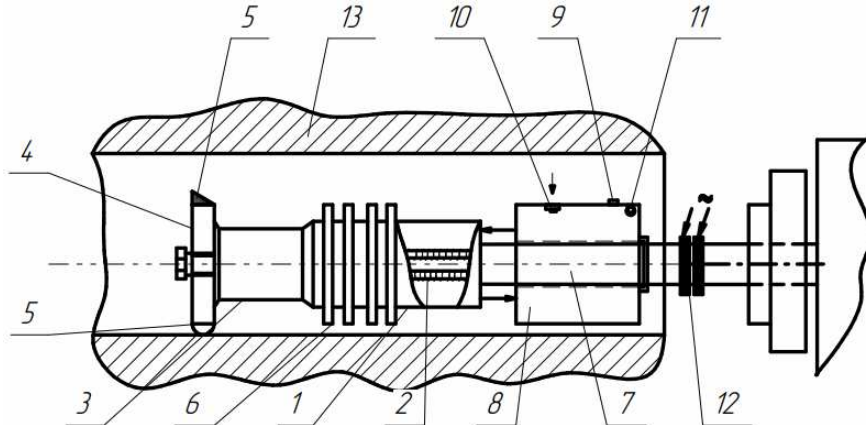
Вариант устройства для точения и финишной обработки внутренних поверхностей деталей ультразвуком: 1 – корпус; 2 – магнитострикционный преобразователь; 3 – концентратор; 4 – съемный излучатель ультразвука; 5 – рабочий наконечник; 6 – ребра корпуса; 7 – борштанга; 8 – съемная емкость; 9 – штуцер для наполнения съемной емкости охлаждающим веществом; 10 – штуцер для слива охлаждающего вещества; 11 – насос; 12 – токосъемные кольца; 13 – деталь
